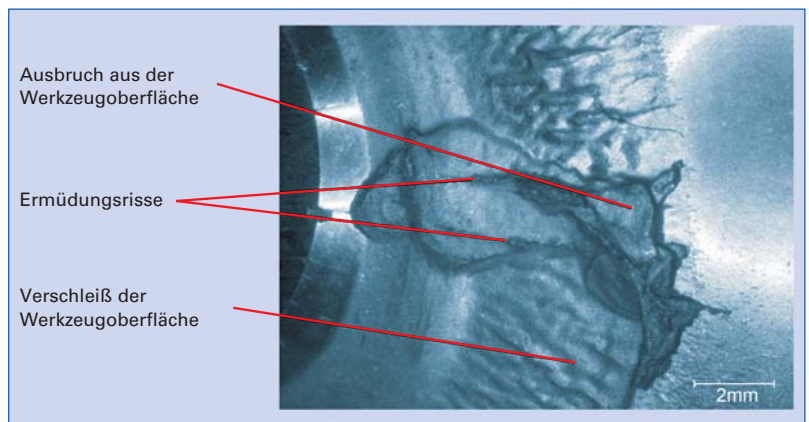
Ermüdungsrisse und Ausbrüche aus der Werkzeugoberfläche in Kombination mit Verschleiß an einem Werkzeugeinsatz zum Kaltfließpressen von Wälzlagerkugellohlingen.
